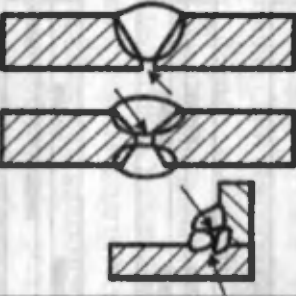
Примеры подготовки кромок для сварки в стыковых соединениях
